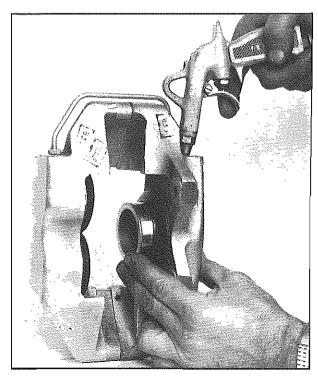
Inserire una pistola ad aria compressa Placing a compressed air gun
